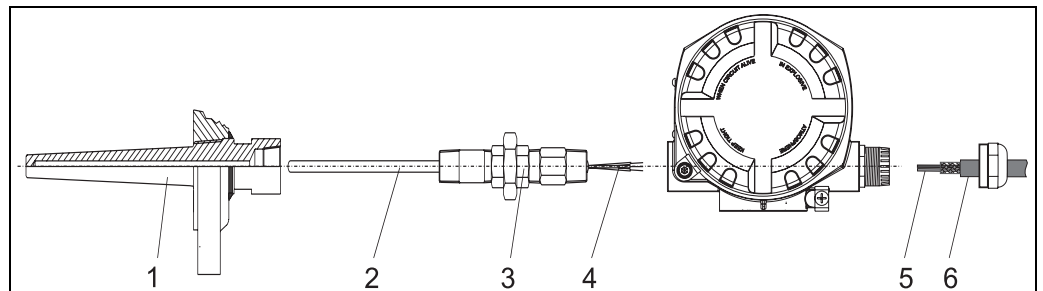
Installazione del trasmettitore da campo direttamente su un sensore
